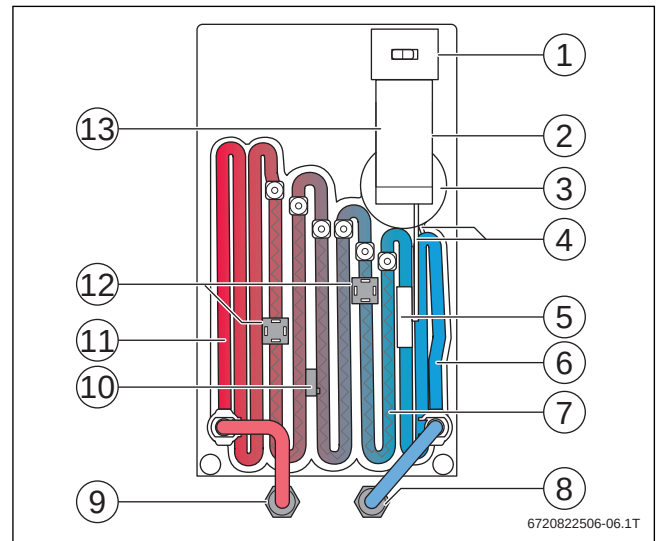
Durchlauferhitzer, hydraulisch gesteuert – mit Blankdrahtheizsystem
